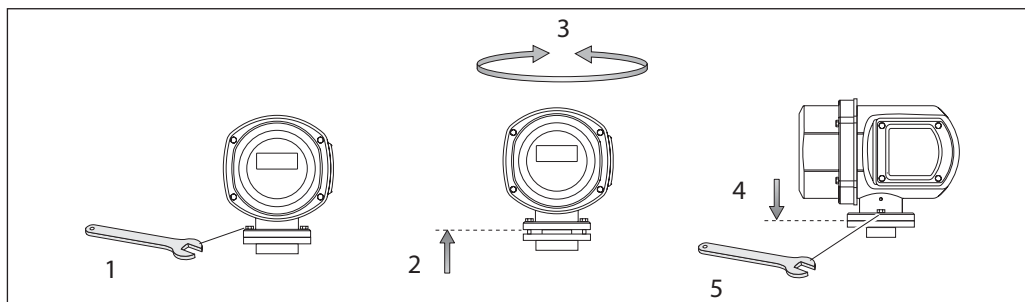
Вращение корпуса трансмиттера (полевой корпус из нержавеющей стали)
